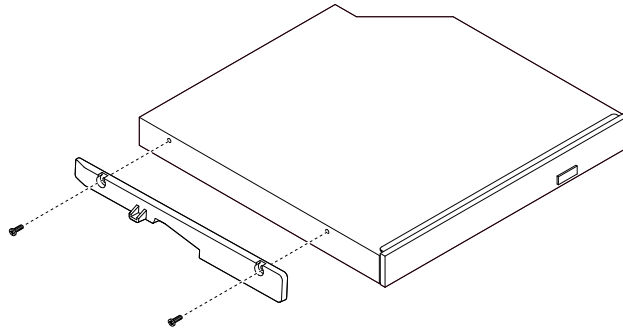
Halterung für flaches optisches Laufwerk entfernen
